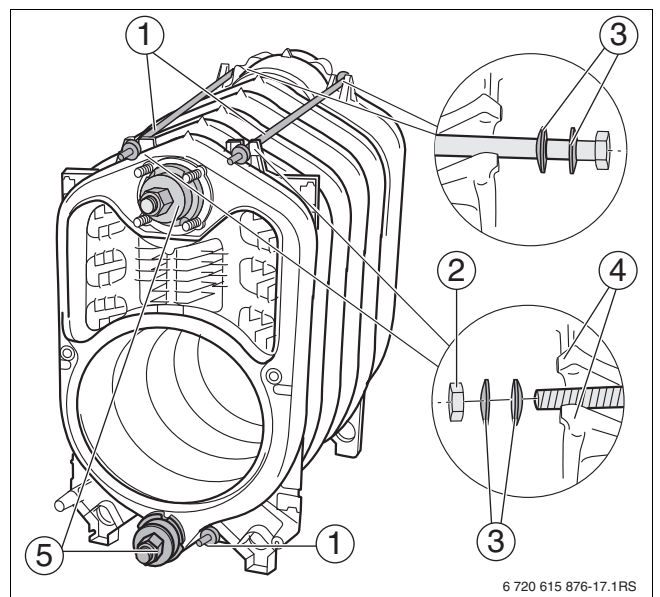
Montaje de los tirantes, disposición de los resortes de disco
